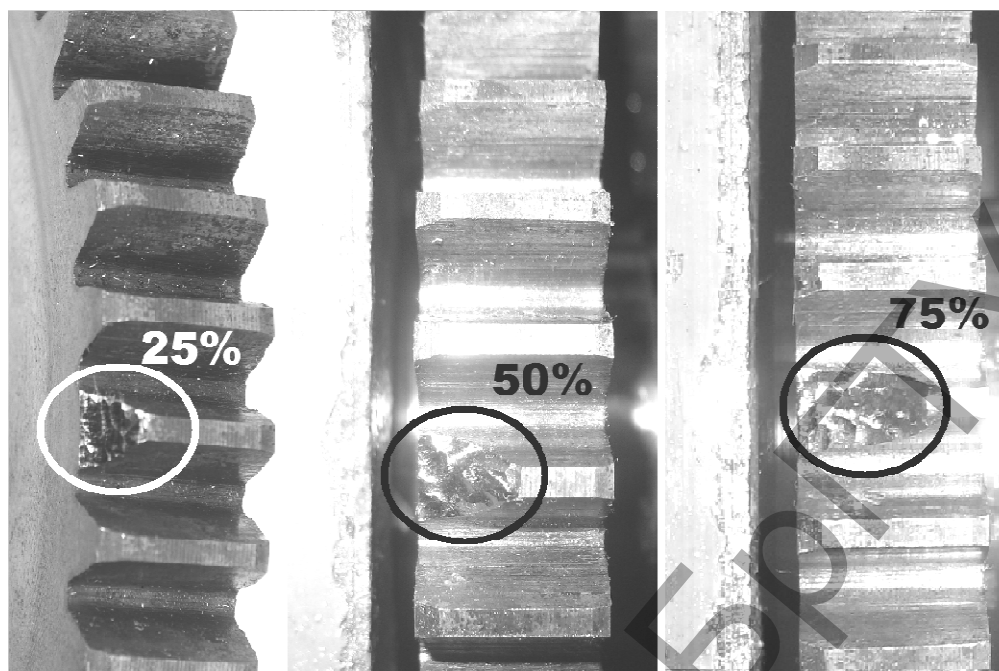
Скол зуба опытного колеса $z=43$ 2-го вала коробки скоростей станка CH-501 25%, 50% и 75% ширины зубчатого венца
